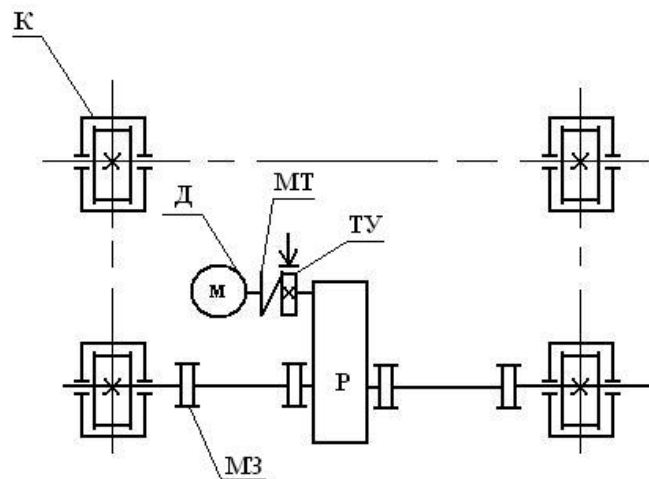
Кинематическая схема механизма передвижения тележки
